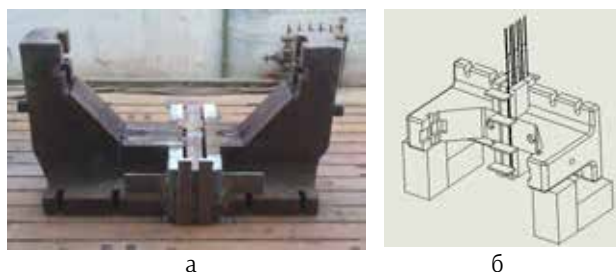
Ремонт корпуса бойка к прессу усилием 5000 тс со сложной, разветвленной трещиной: а – корпус бойка, после разделки трещины механической обработкой, собранный с центральной вставкой под ЭШС, б – положение детали при ЭШС
